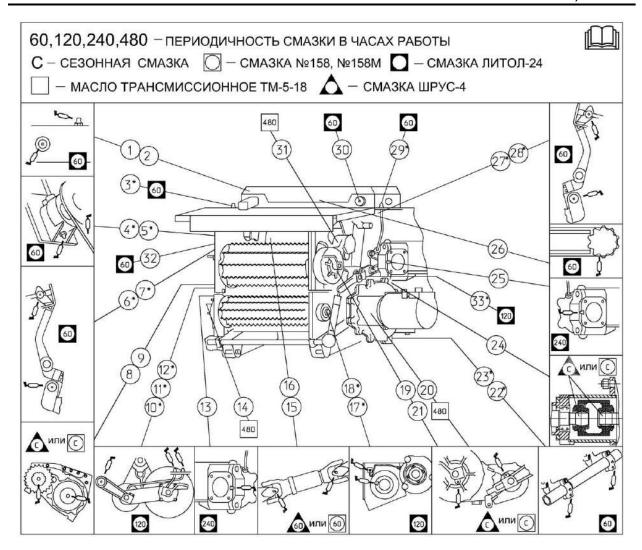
Схема смазки питающе - измельчающего аппарата измельчителя
